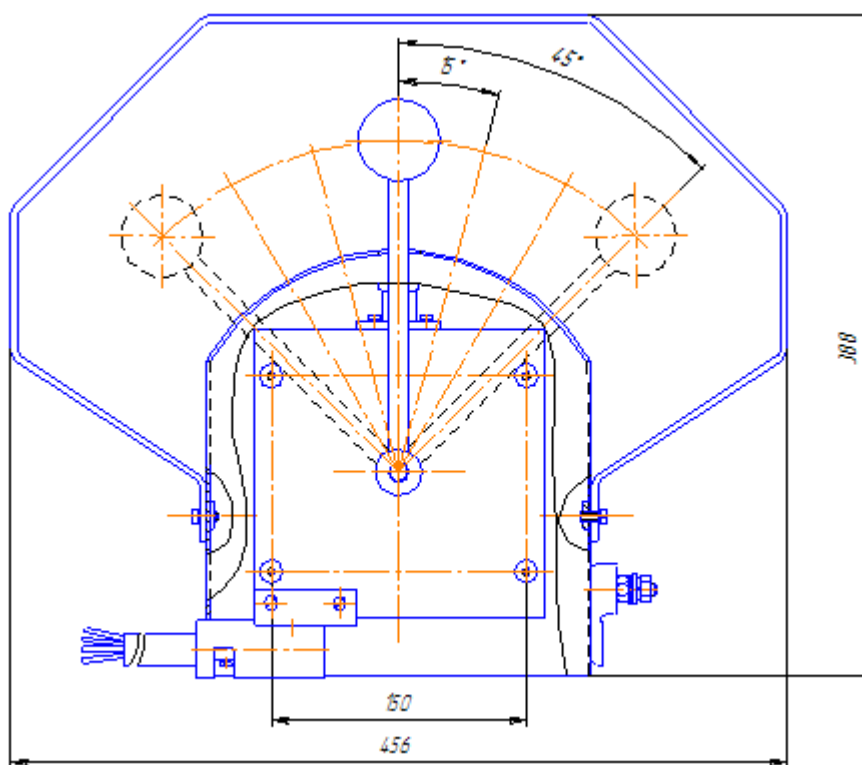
Габаритные и присоединительные размеры КАГВ
